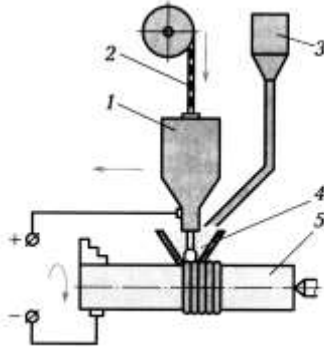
Схема електродугового наплавлення циліндричної поверхні деталі під флюсом
